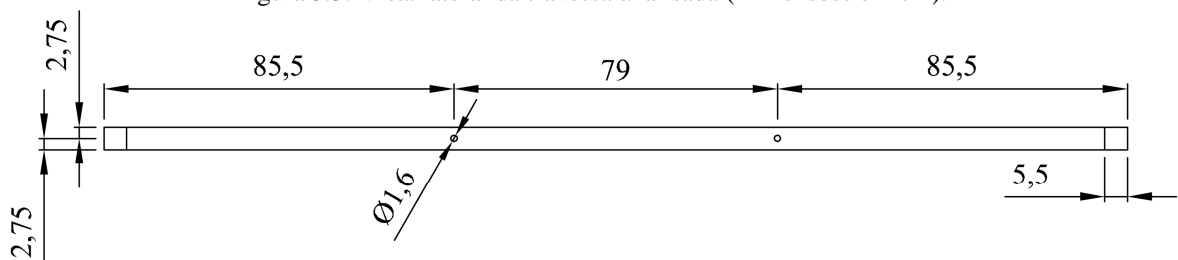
Vista superior da travessa analisada (Dimensões em cm).
